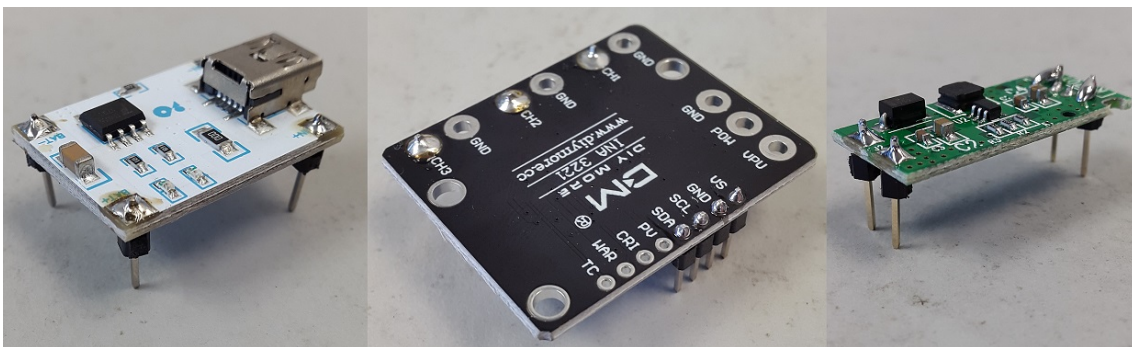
Referencia de soldadura de algunos componentes.
